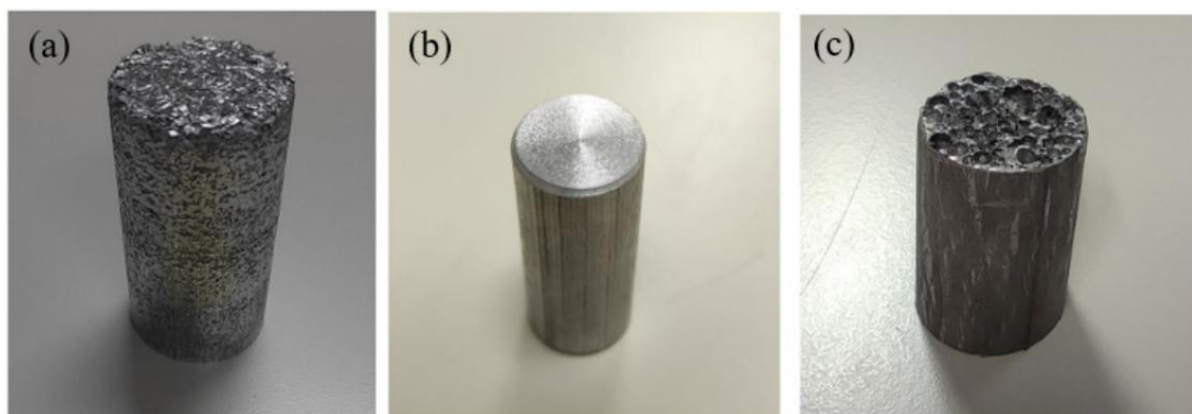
Стадии производства металлической пены на основе металлической стружки [4]: а – заготовка, б – спрессованная заготовка, с – пористый металл после нагрева.
